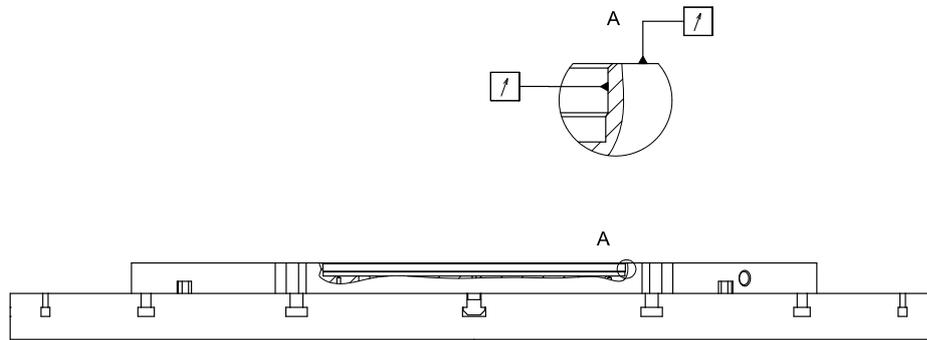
Rund- und Planlauf der Grundplatte prüfen
